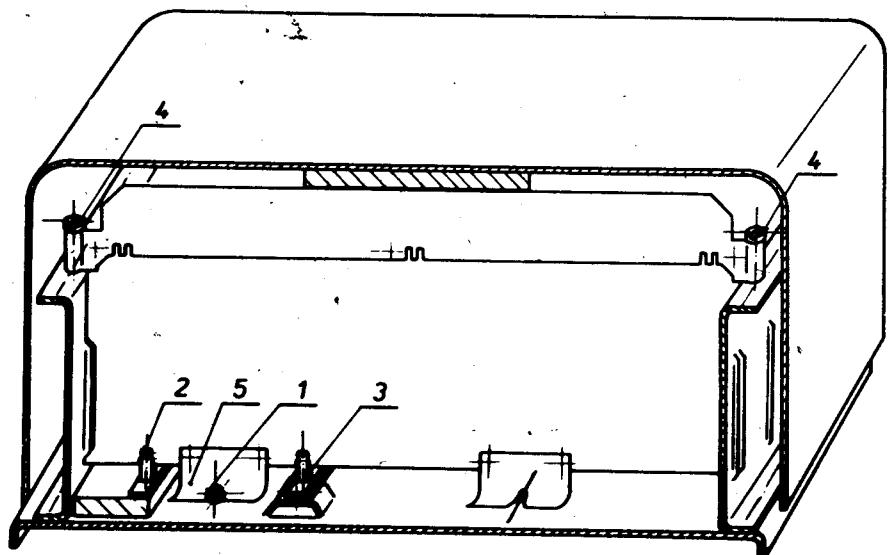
Otočné uspořádání rozvodnice se zesilovací soupravou
